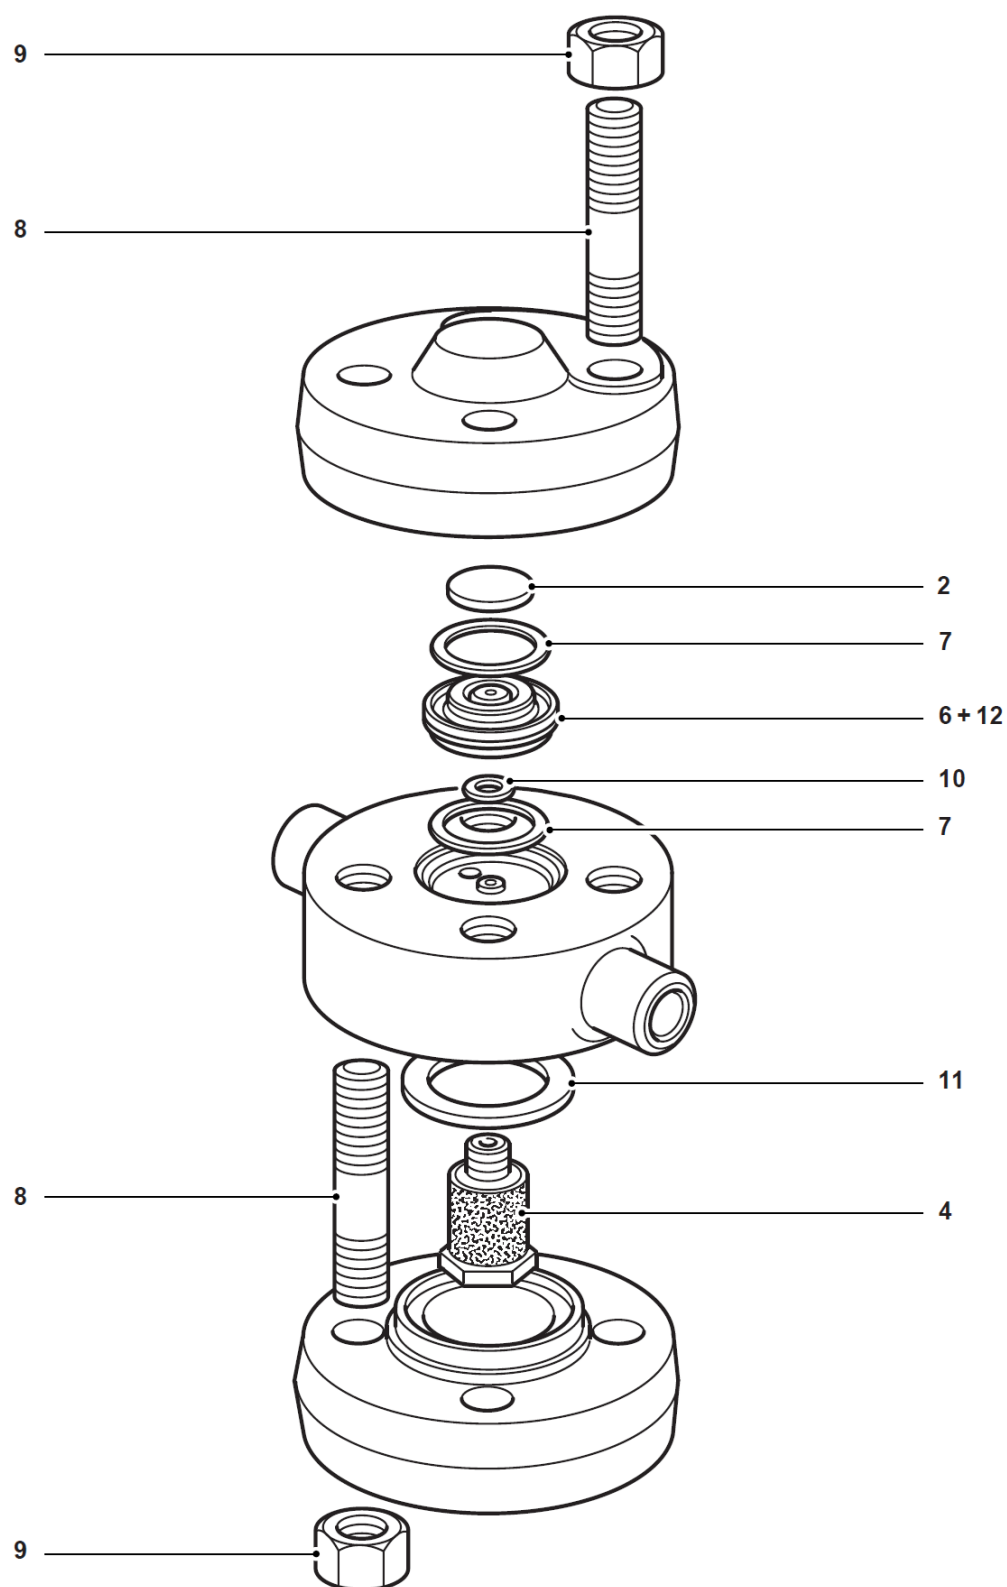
TD120M avec des raccords à souder butt weld
